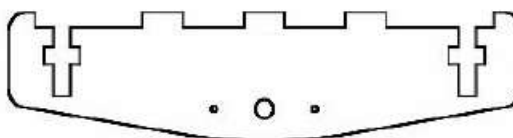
Ліва бокова частина вертикальної платформи
